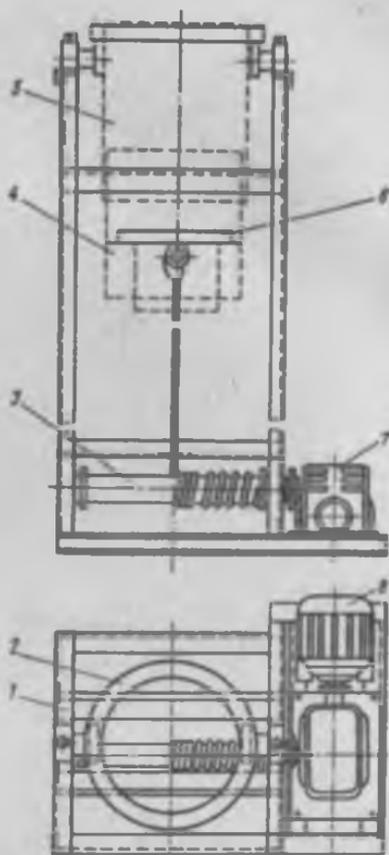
Приспособление для выпрессовки питательной коробки кипятильников
